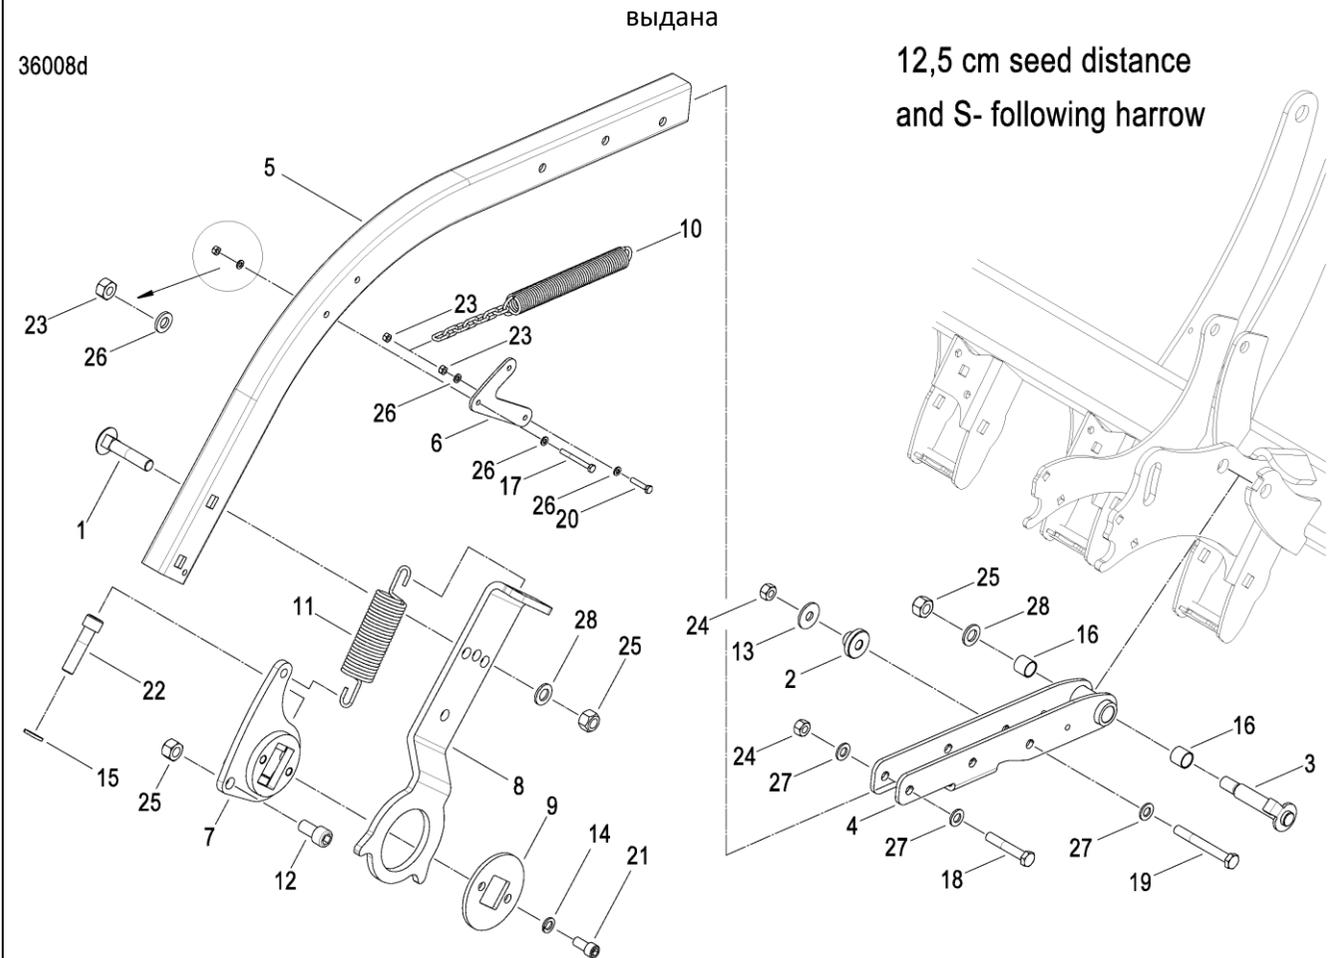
Держатель устройства загорточного ОТИБ.271149.026
